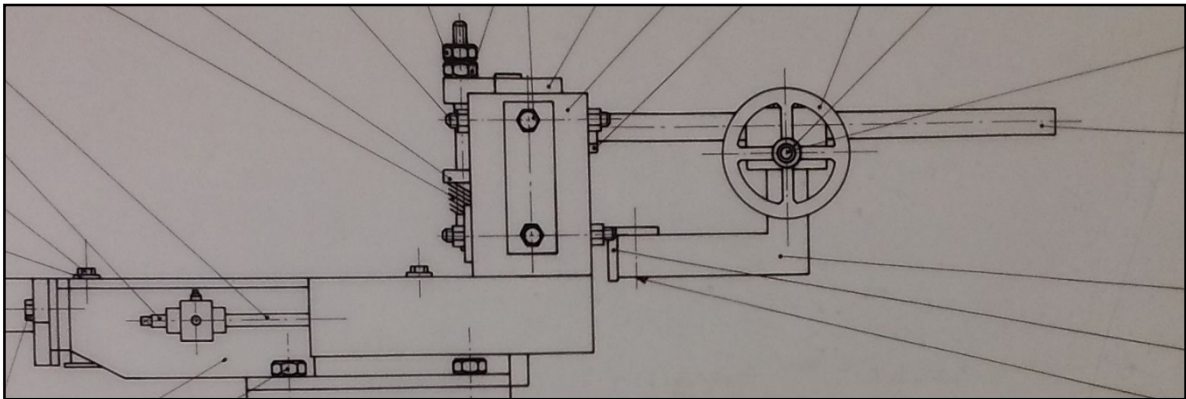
Vista lateral de las barras guías del plano A0-500 Conjunto cizalla mecosoldada.
